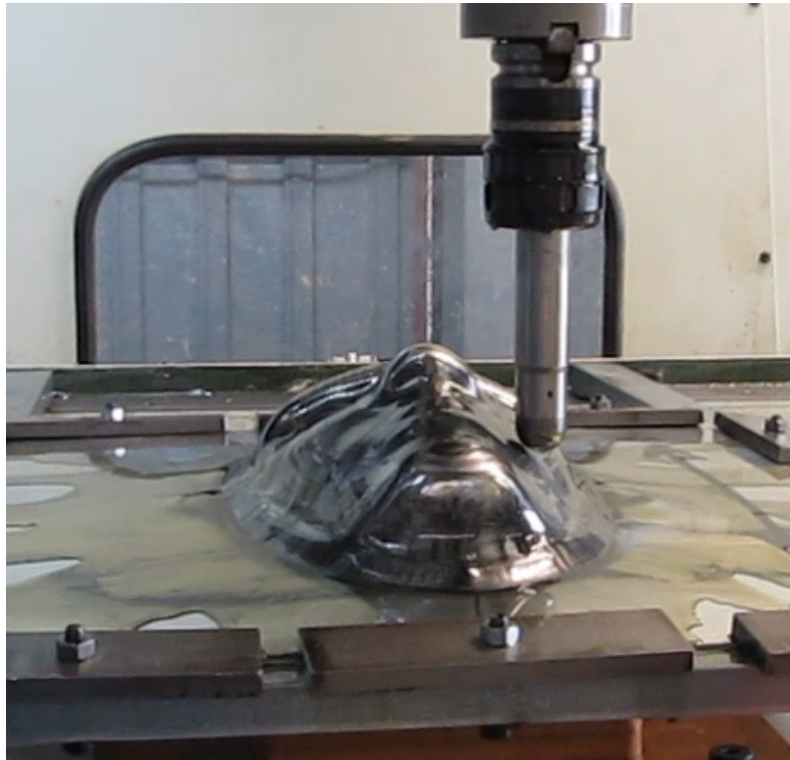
Зовнішній вигляд станда двох інструментальний метод пошарового локального деформування
